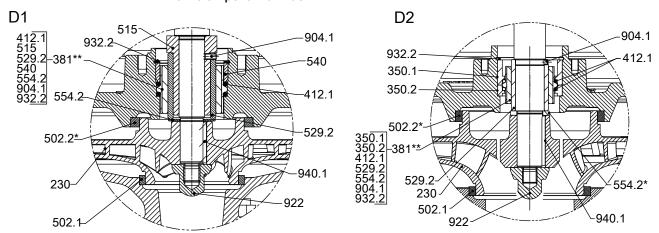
Детальное изображение проточной части (в зависимости от типоразмера подшипниковой опоры)
